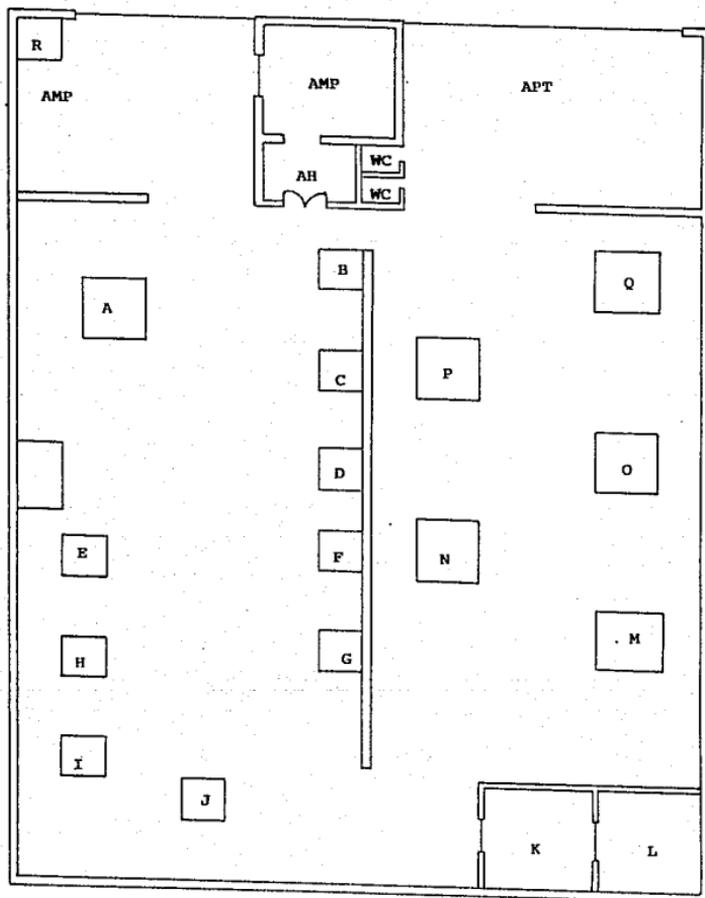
DISTRIBUCION DE PLANTA
